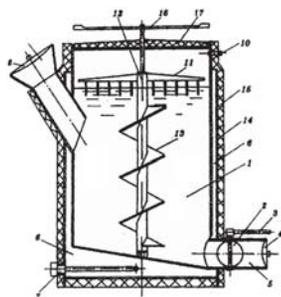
Схема-разрез биореактора-метантенка ИБГУ-1: 1 — корпус биореактора; 2 — диафрагма; 3 — рукоятка; 4 — затвор; 5 — шлюз для выгрузки сброженной массы; 6 — корпус тепловой рубашки; 7 — электрический ТЭН; 8 — герметический затвор; 9 — загрузочный люк; 10 — газовый штуцер; 11 — гребенка; 12 — вал; 13 — шнек; 14 — облицовка теплоизоляции; 15 — теплоизоляция; 16 — рукоятка-крестовина мешалки; 17 — крышка биореактора. Принцип термостата
